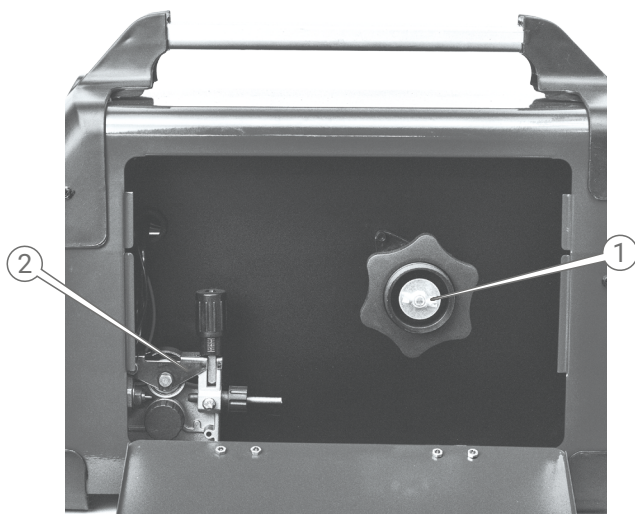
Відсік для зварювального дроту (вид збоку).
